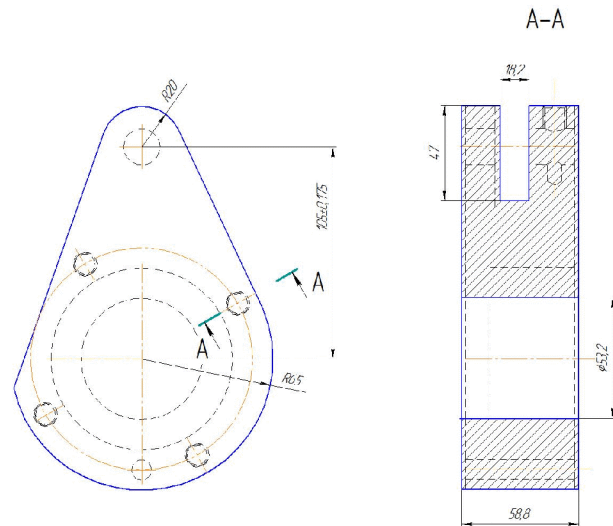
Ескіз вилівка в піщано-глинисті форми
